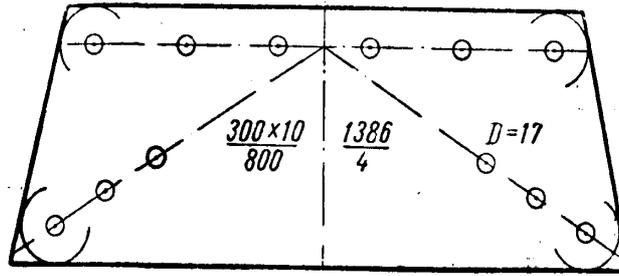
Шаблон на контур сварного элемента и 12 отверстий
